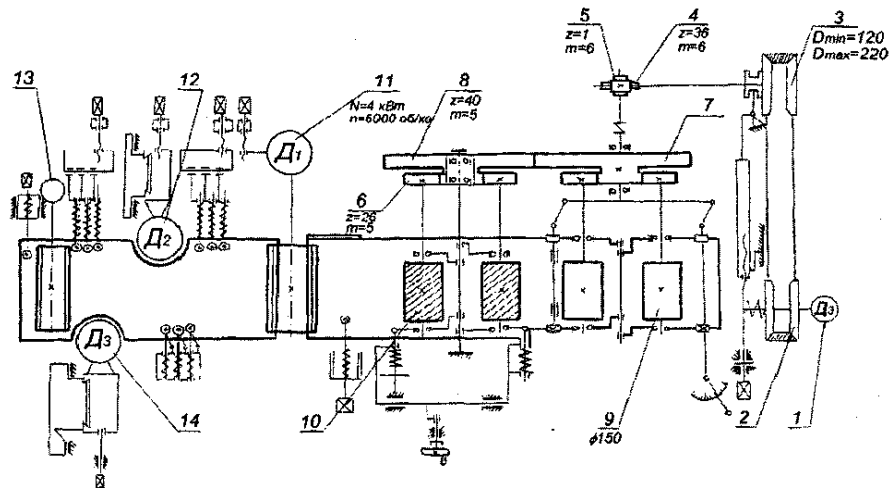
Кінематична схема чотирибічного поздовжньо-фрезувального верстата моделі С16-1А: 1 -електродвигун подачі; 2, 3 - варіатор; 4, 5 - черв'ячний редуктор; 6, 7, 8 -шестірні; 9 - нижні подавальні вальці; 10 - верхні подавальні вальці; 11 - привод нижньої горизонтальної головки; 12, 14 -привід вертикальних головок; 13 - привод верхньої горизонтальної головки
